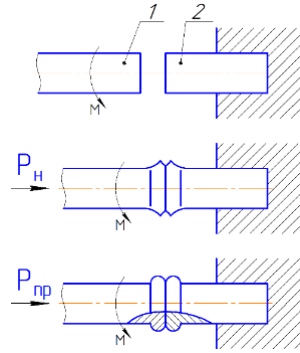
Принципиальная схема сварки трением 1 – вращающаяся заготовка, 2 – неподвижная заготовка
